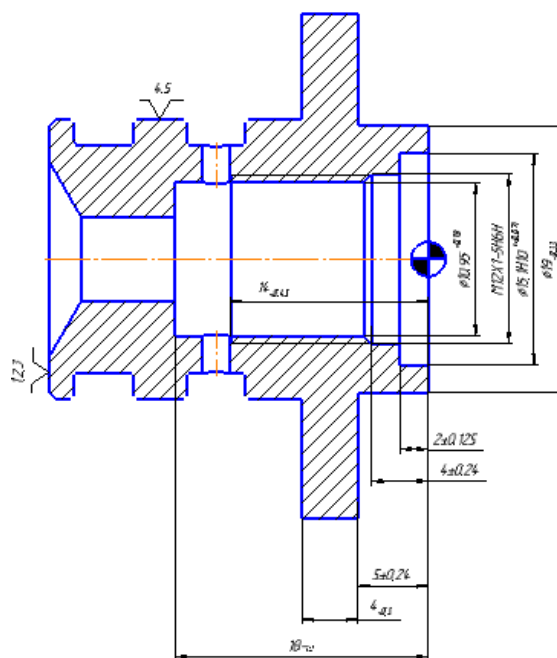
Схема базирования заготовки операция 010 установ Б
